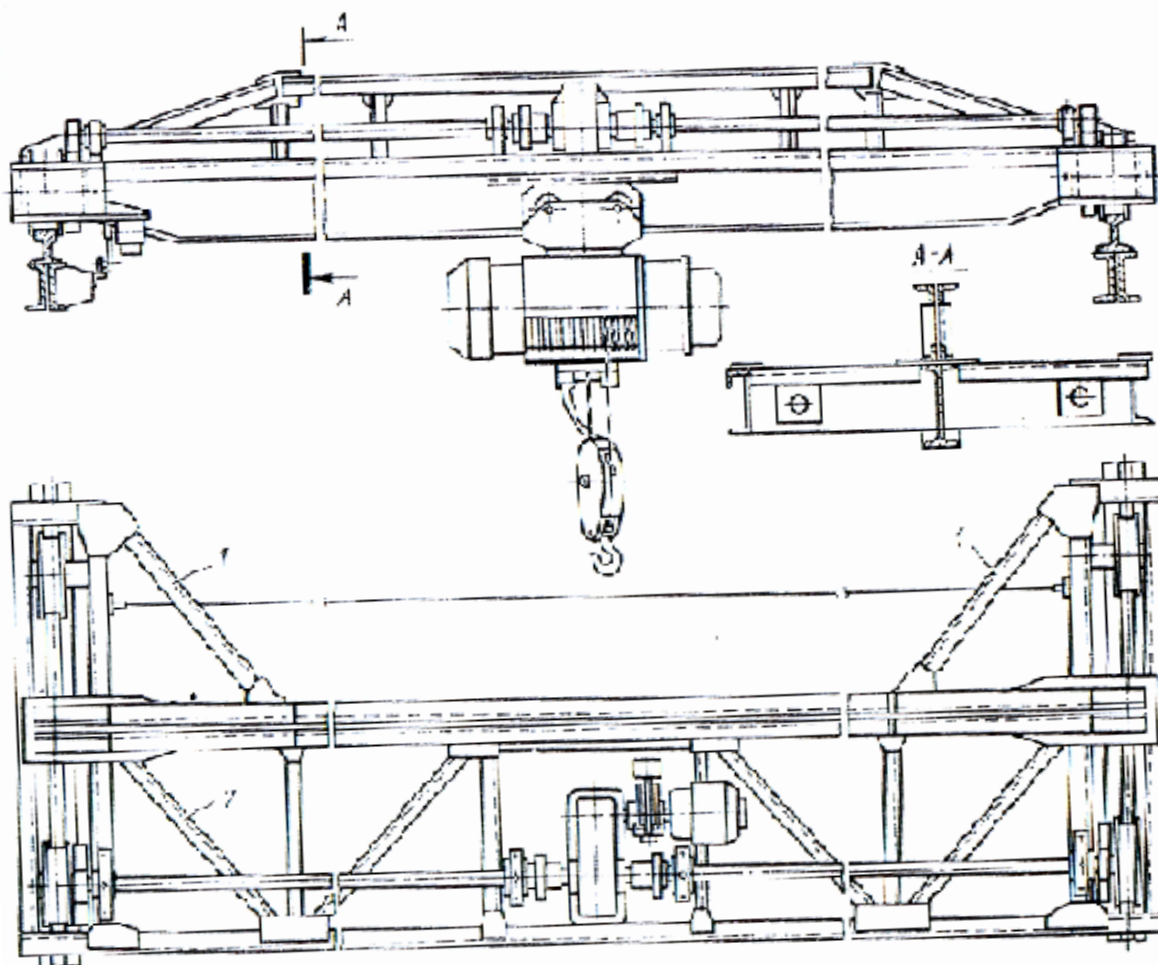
Общий вид однобалочного мостового крана опорного типа сварной и клёпаной конструкции:
